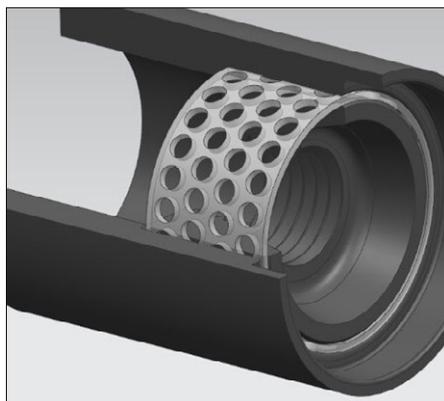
Schnitt des Entwurfs der Induktionsschweissschelle bestehend aus Stopfen, Stahlring mit Löchern und Rohr.
